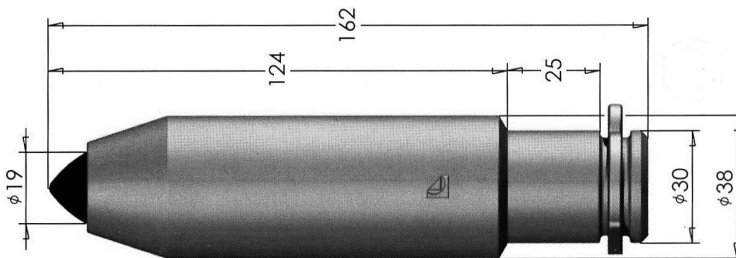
Резец тангенциальный поворотный марки РШ 38-75/19.М2
